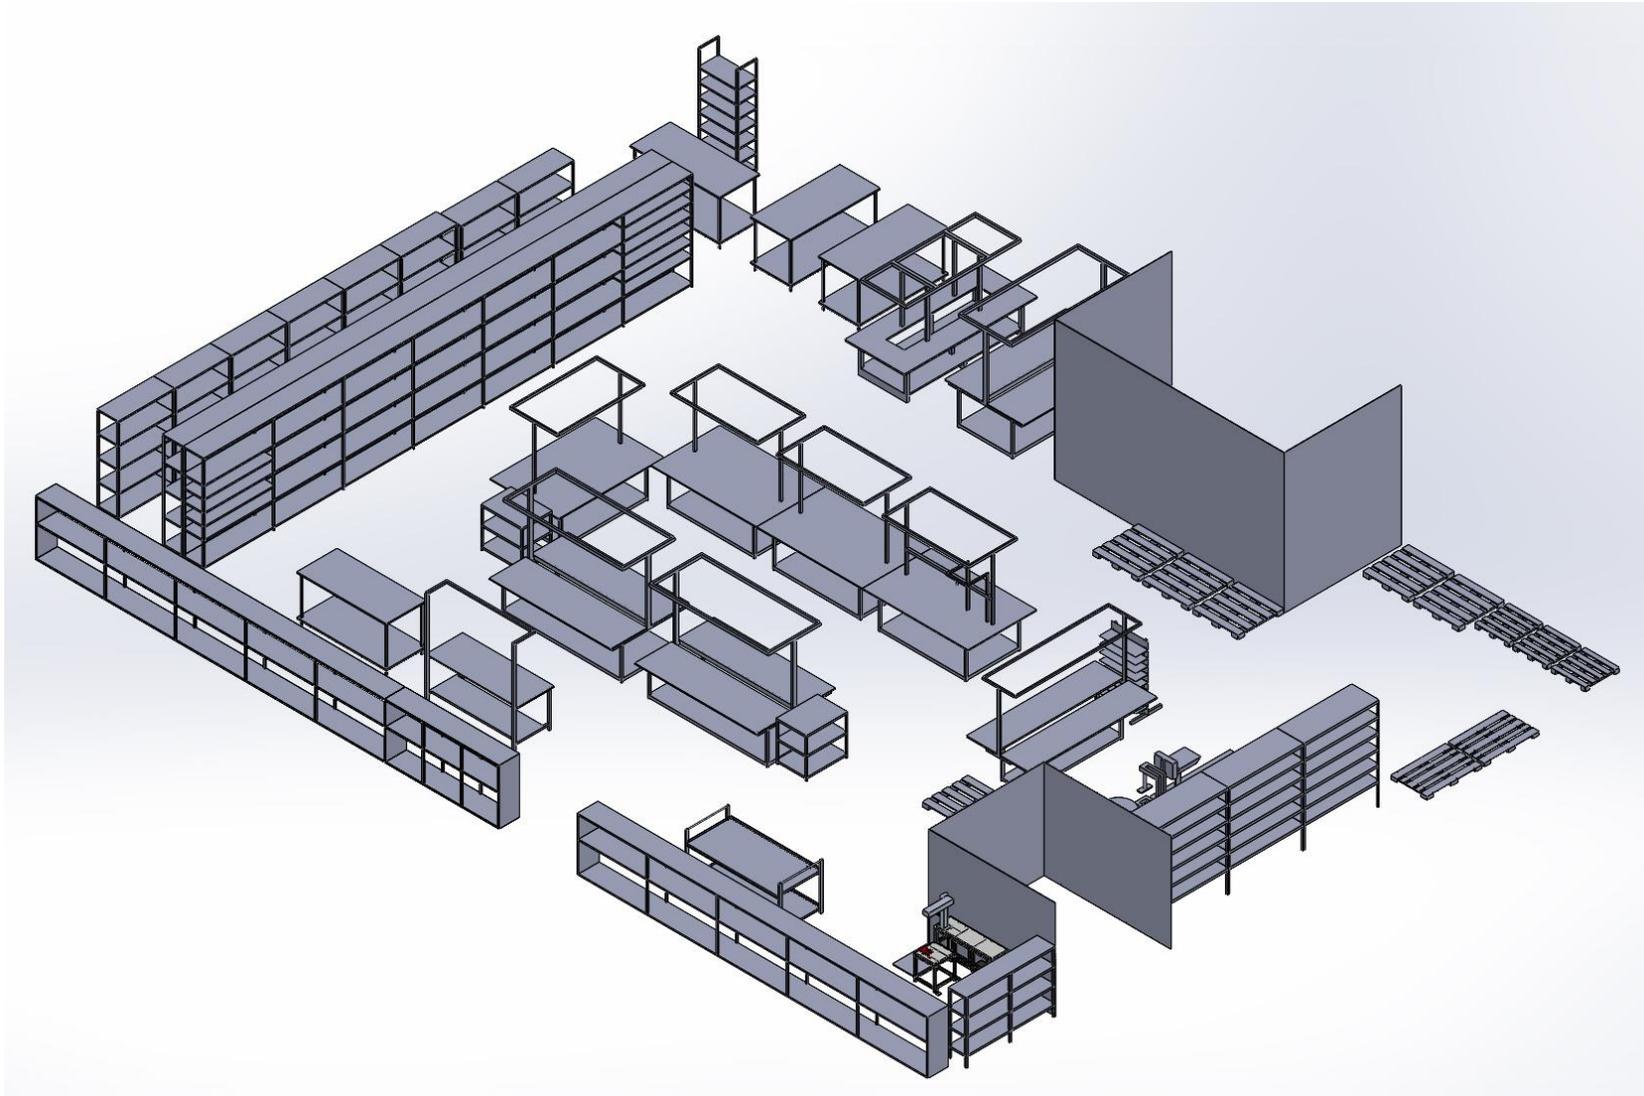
Layout 3D da Secção de Montagem Comercial (do autor)
